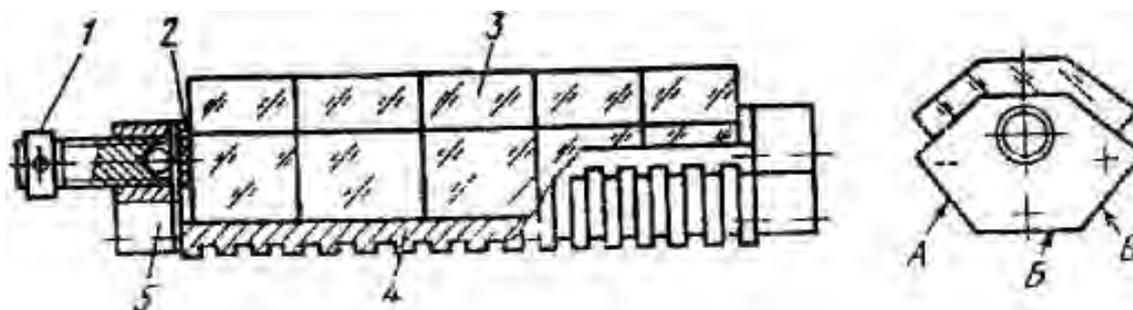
Приспособление для механического крепления призм сжатием
